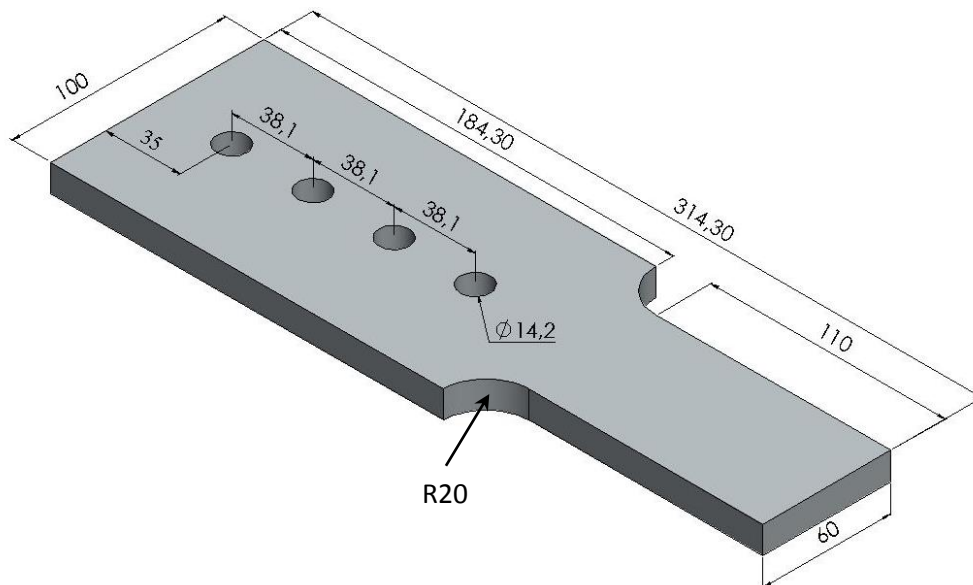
Chapa de fixação para a instalação de perfis com 1 furo por seção, dimensões em (mm)
